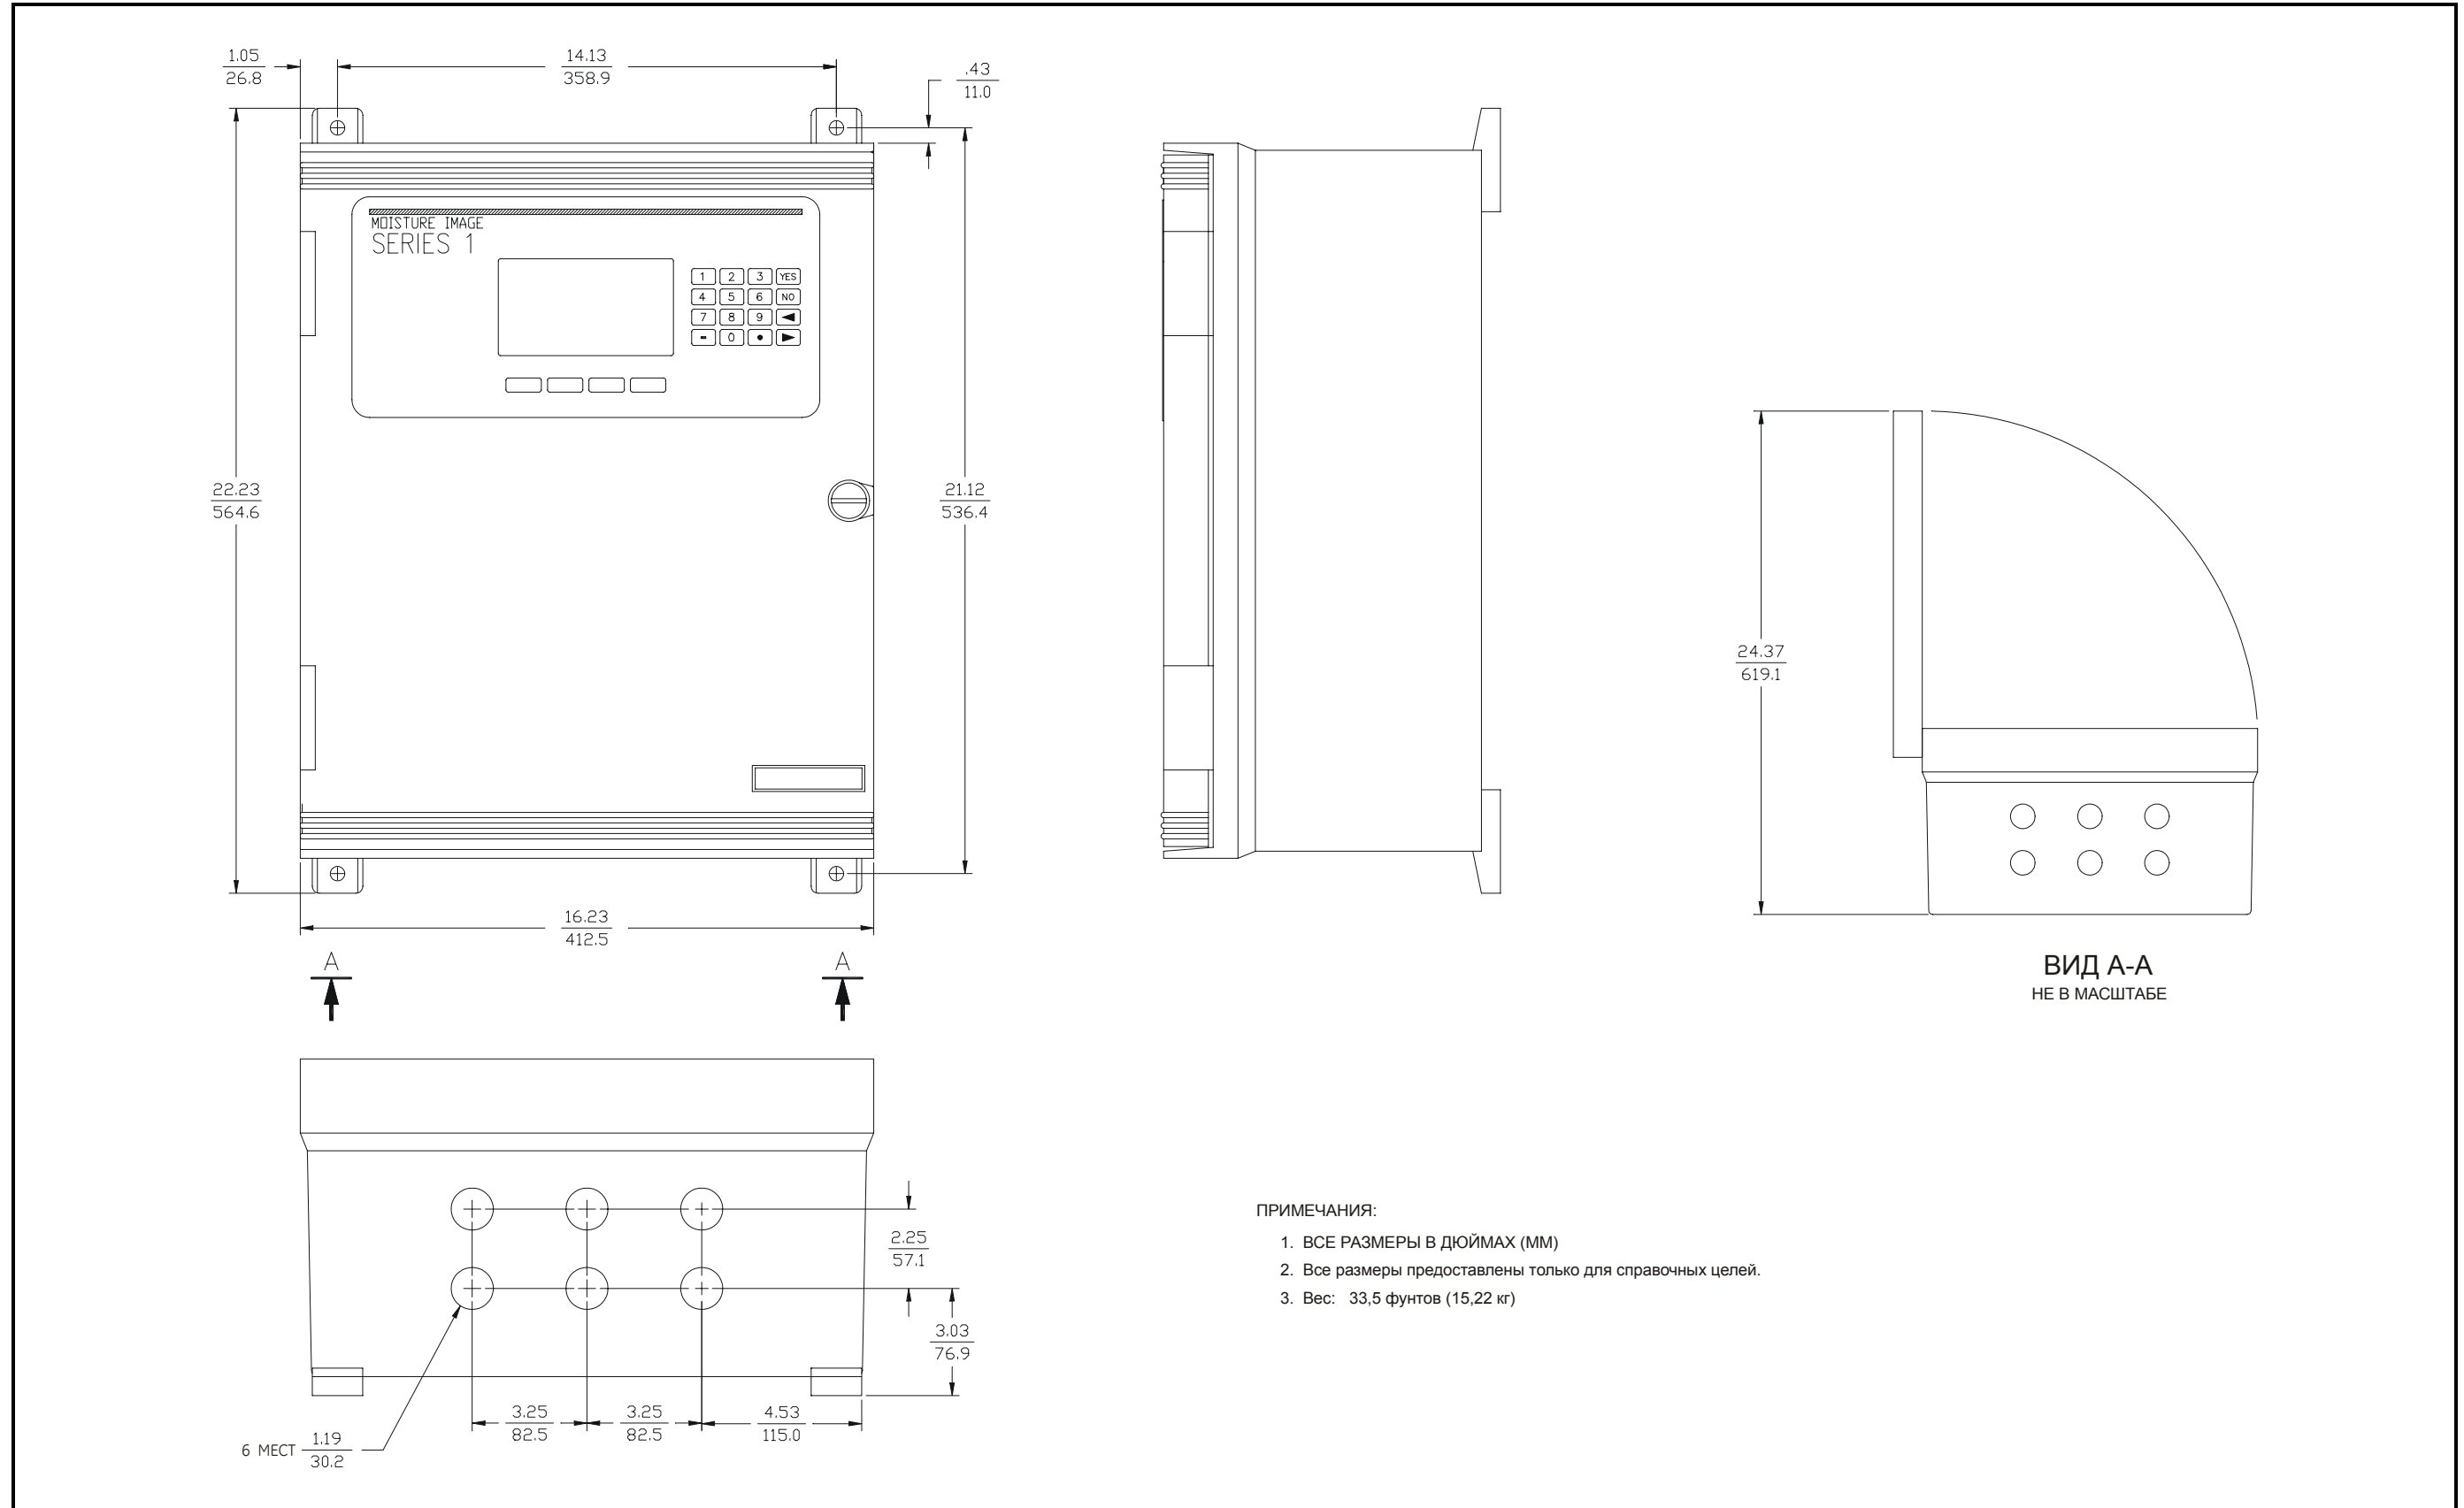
Контурный чертеж и установка прибора Moisture Image Series 1 для панельного монтажа (чертеж #712-234)
